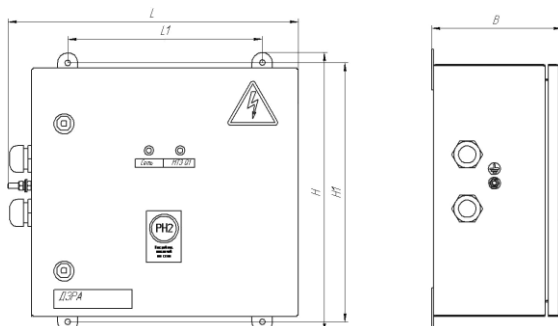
Общий вид, габаритные и установочные размеры АОШ-Х-Х-38В (1,6-10 кВА)
